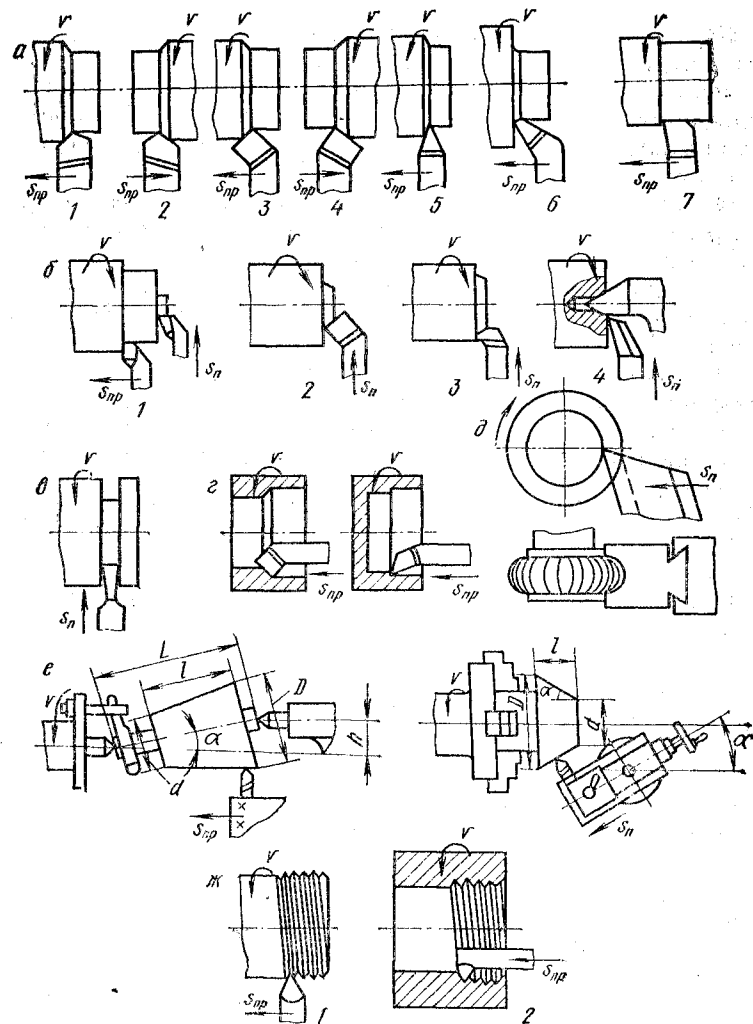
Токарные резцы и схемы обработки поверхностей заготовок на токарно-винторезном станке
